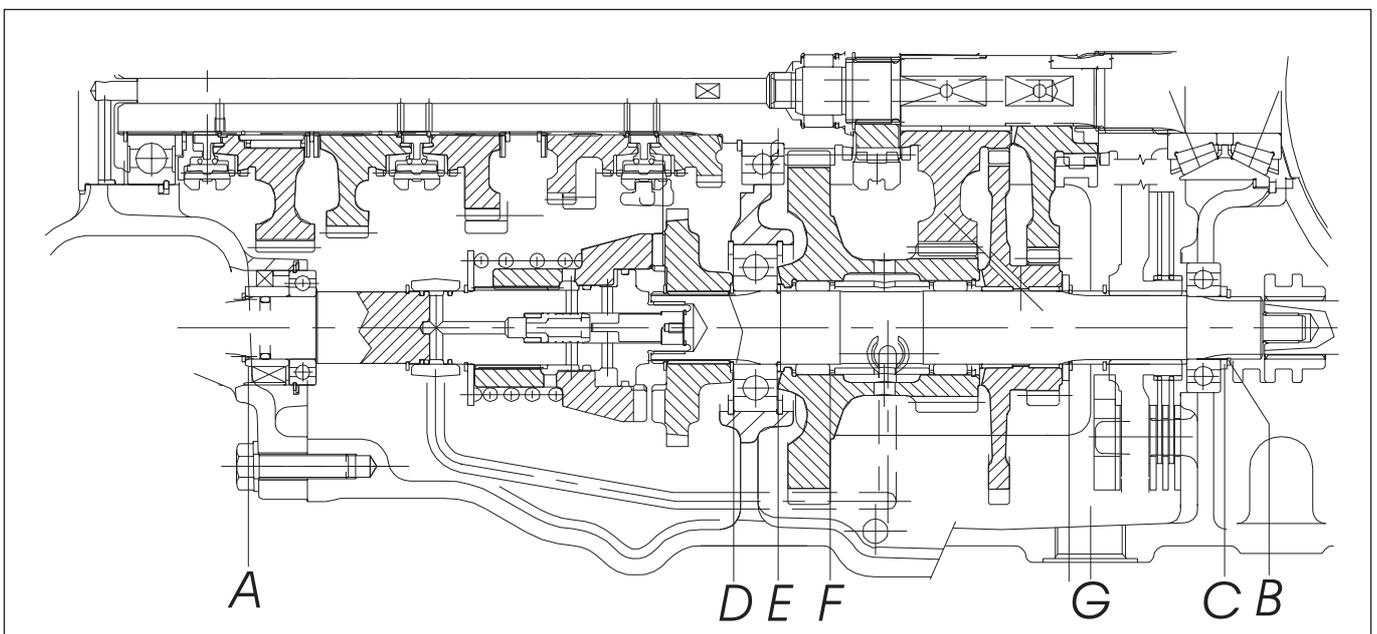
Ensemble de prise de force pour les roues motrices avant.
